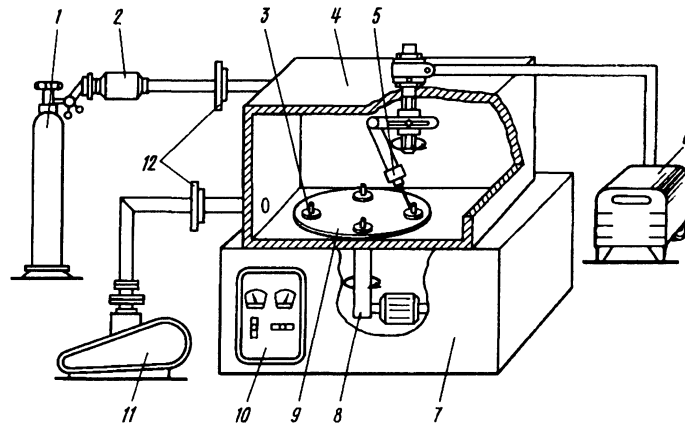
Установка для сваркопайки вольфрама с медью:
